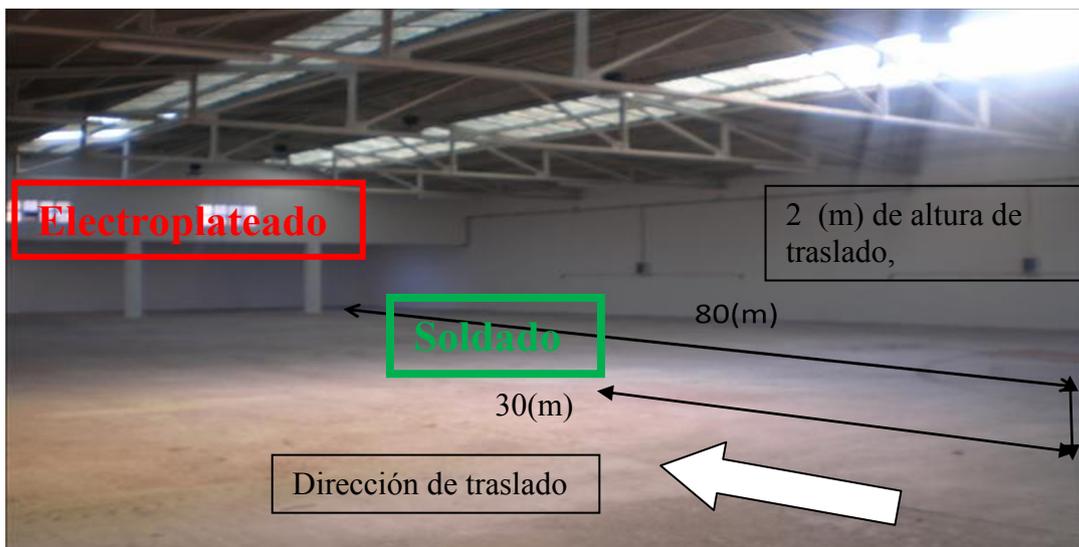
Ubicación zonas electro-plateado y soldado.
